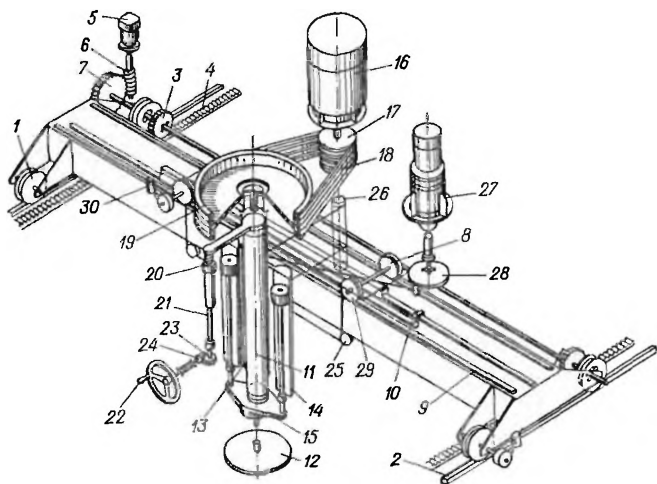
Кинематическая схема шлифовально-полировального мостового станка модели СМР-013
